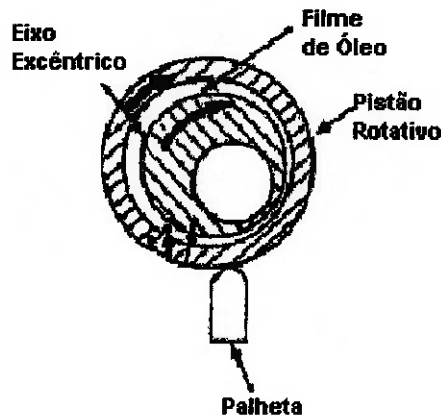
Detalhe da montagem do eixo excêntrico com o pistão rotativo.
